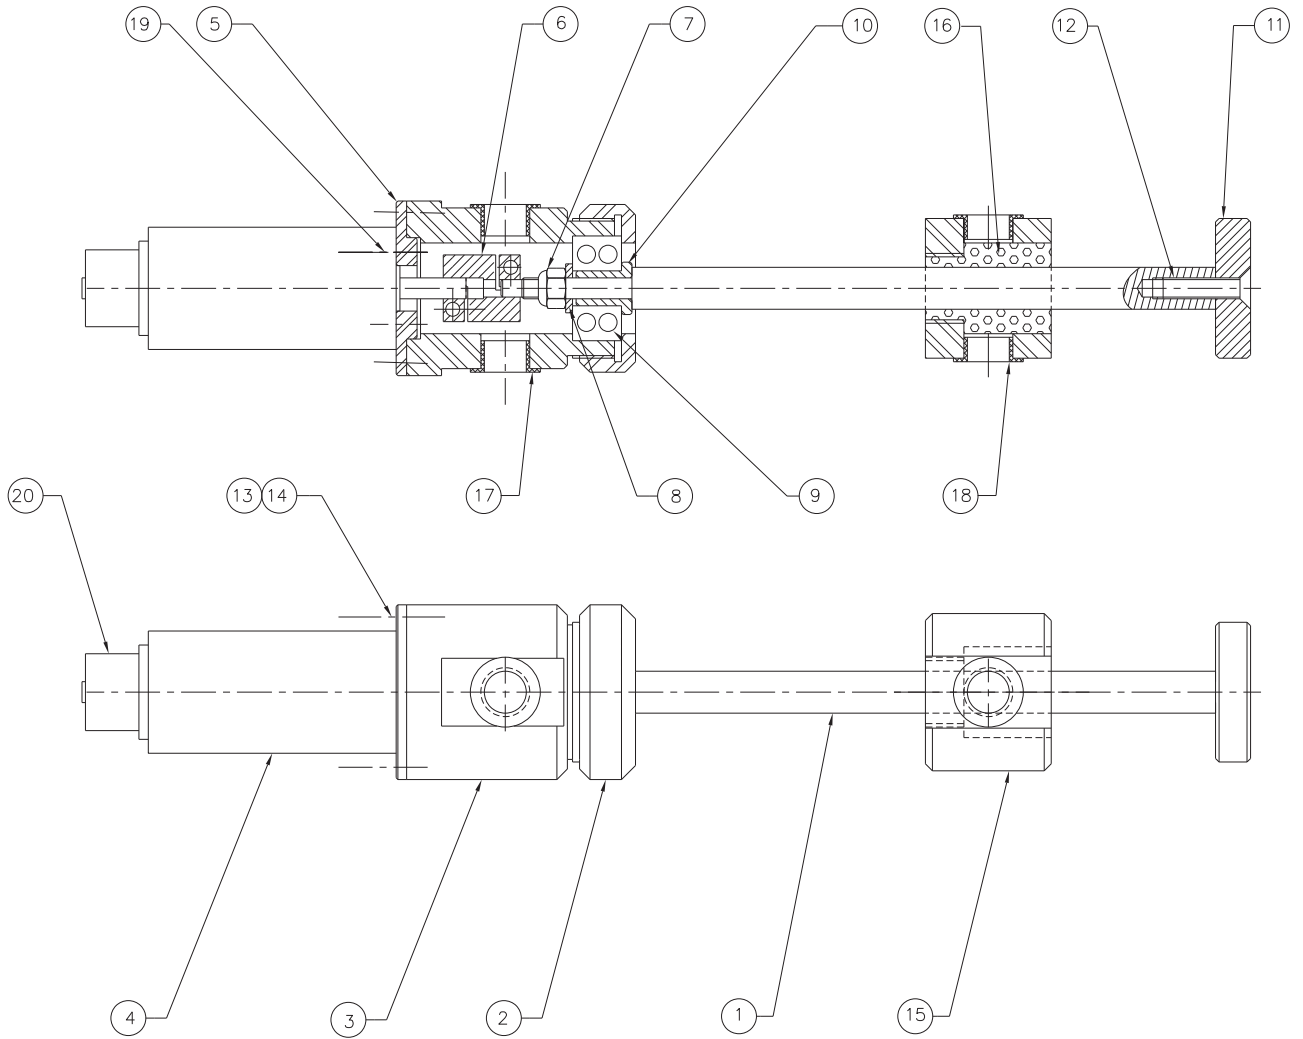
Dessin de l'ensemble moteur + axe moteur + vis
